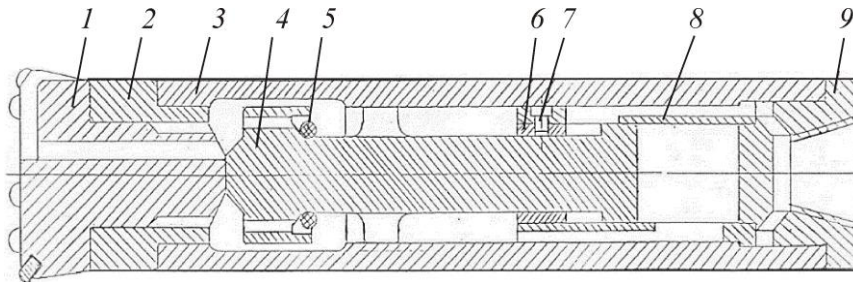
Схема погружного пневмоударника П110ГМ с эластичным клапаном на ударнике: 1 — буровая коронка; 2 — букса; 3 — корпус; 4 — ударник; 5 — эластичный клапан; 6 — полукольца; 7 — стопор; 8 — гильза; 9 — переходник
